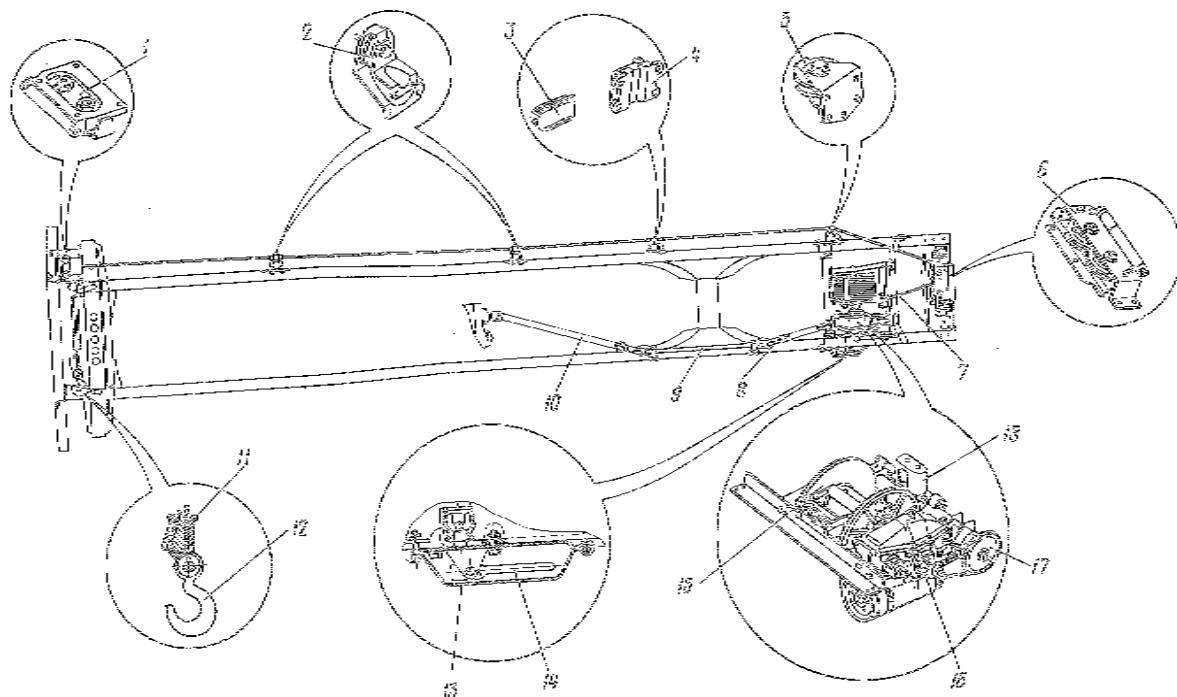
Лебедка: 1 — направляющие передние ролики; 2 — опорные ролики (первый и второй); 3 — клин; 4 — кронштейн клиновой заделки троса; 5 — опорный третий ролик; 6 — направляющие задние ролики; 7 — трос; 8 — карданный задний вал; 9 — карданный промежуточный вал; 10 — карданный передний вал; 11 — клин коуша; 12 — крюк; 13 — крышка; 14 — рычаг отключения вала барабана; 15 — барабан лебедки; 16 — редуктор; 17 — ведомая звездочка; 18 — тросоукладчик
